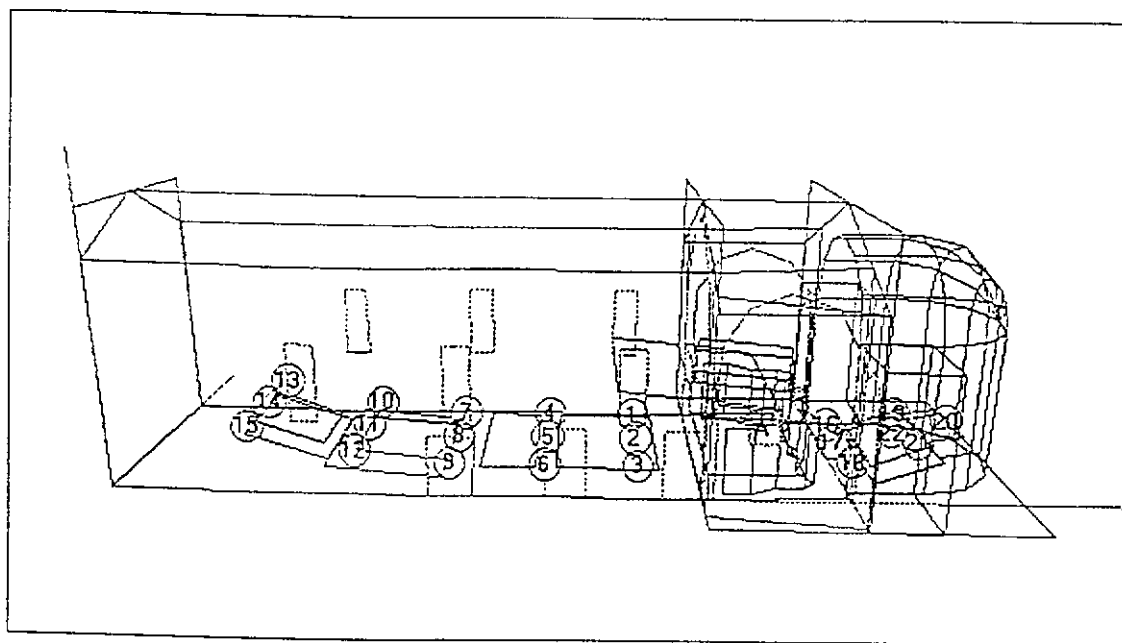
Ipotesi di allestimento "E". Vista prospettica.
